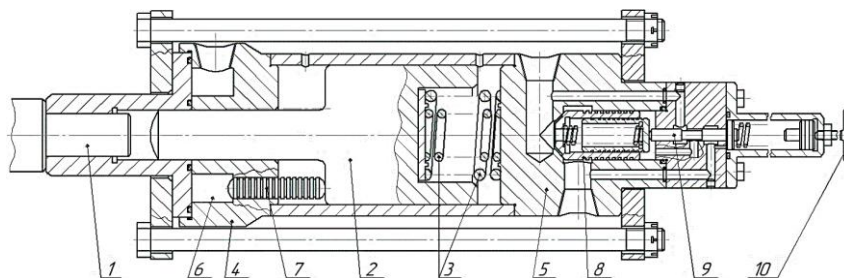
Конструктивна схема віброударного пристрою для руйнування гірських порід
